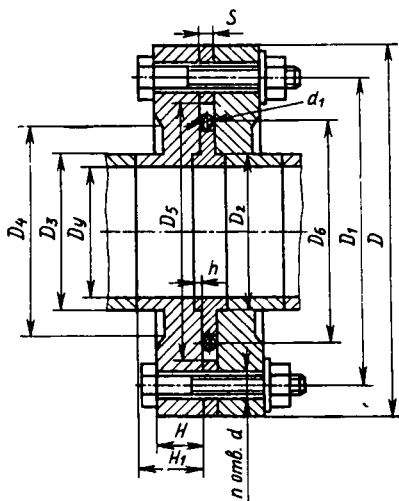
Конструкция разборного соединения с симметричными фланцами и резиновыми прокладками
